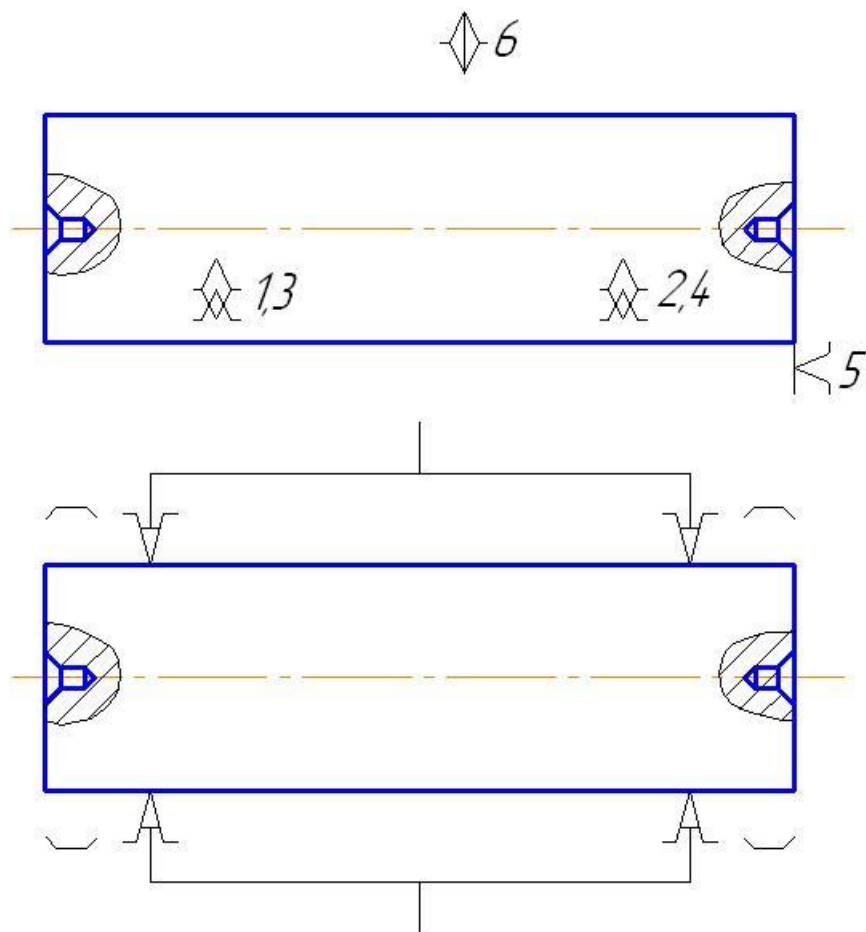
Базирование заготовки в призмах на фрезерно-центровальном станке
